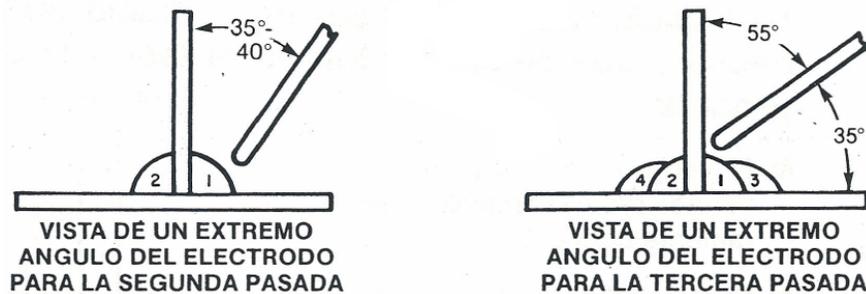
ORDEN DE DEPÓSITO DE LAS SOLDADURAS.
